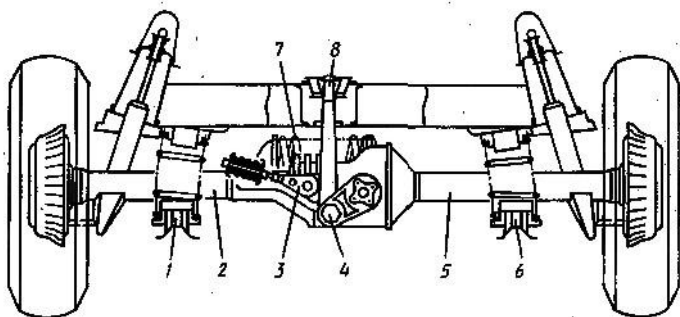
Вид спереди на одношарнирную подвеску с качающимися полуосями фирмы «Даймлер-Бенц» с дестабилизирующей пружиной 7, расположенной над картером главной передачи
